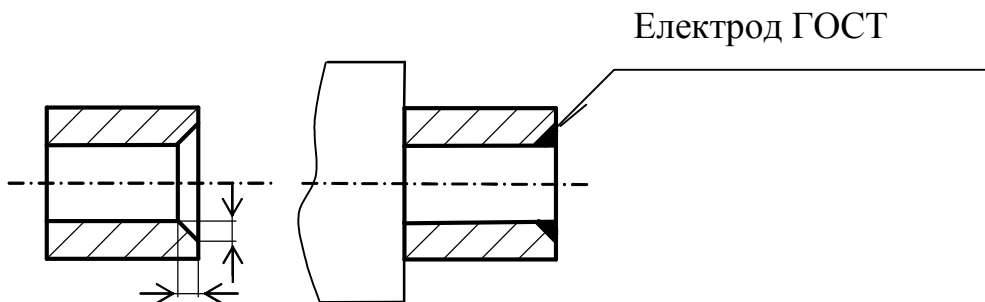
Схема підготовленої до зварювання кромки
